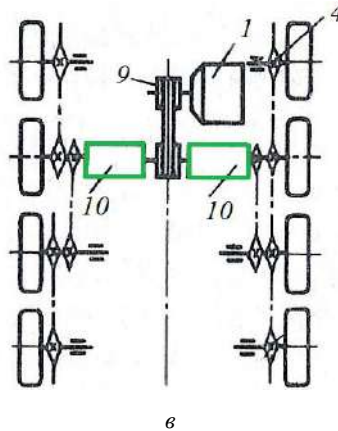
Схеми рулевих керувань автомобілів з неповоротними колесами та механізмами повороту:
